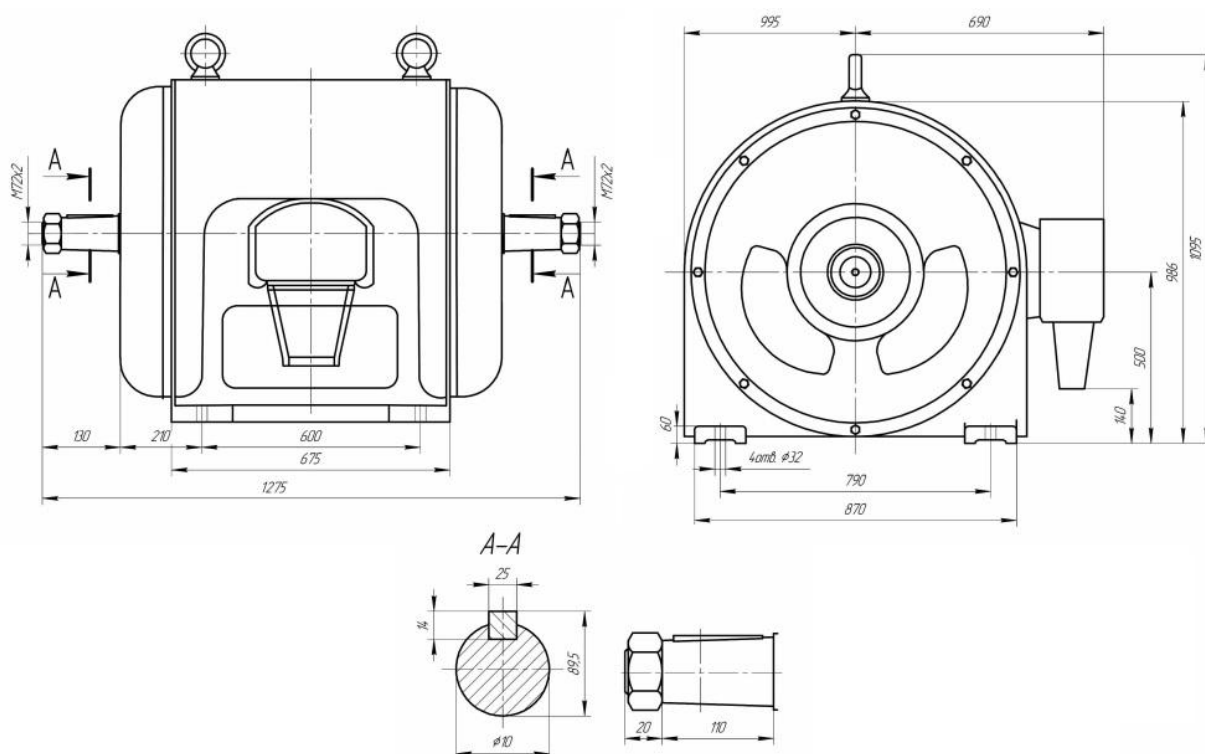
Двигатель АЭ-113-4. Форма исполнения - IM1004.
